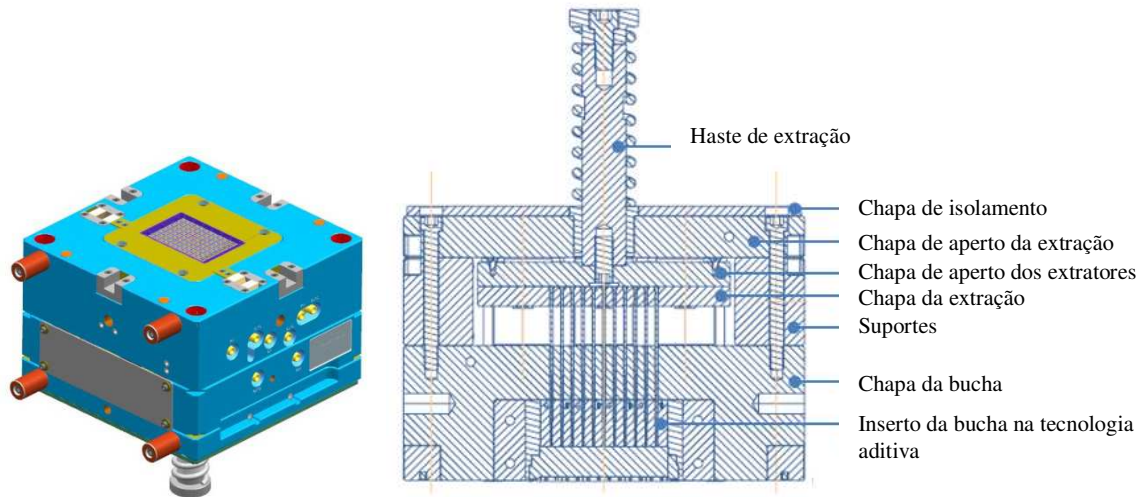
Vista e corte transversal do lado da extração do molde de fabrico aditivo
